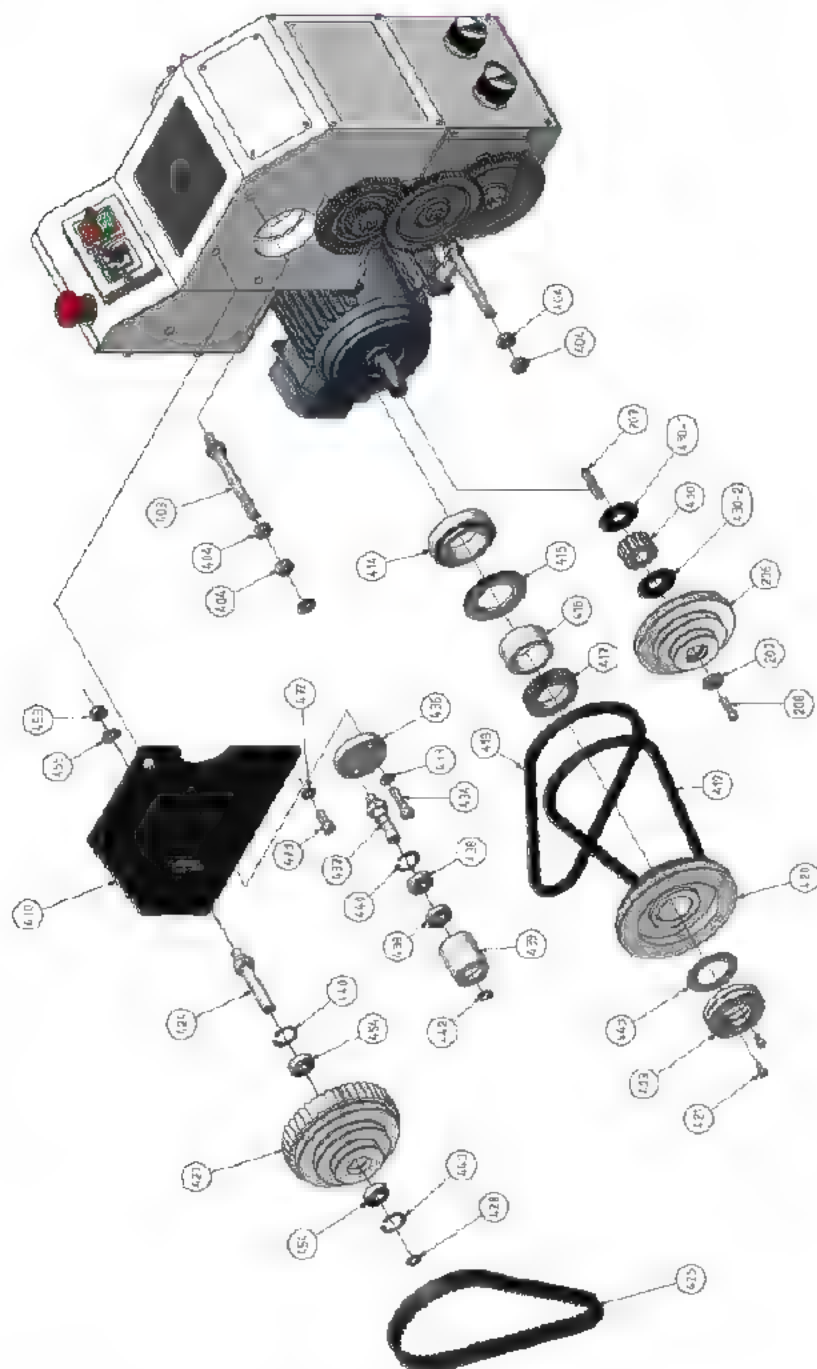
Spindelstock 1 von 2 - Headstock 1 of 2
